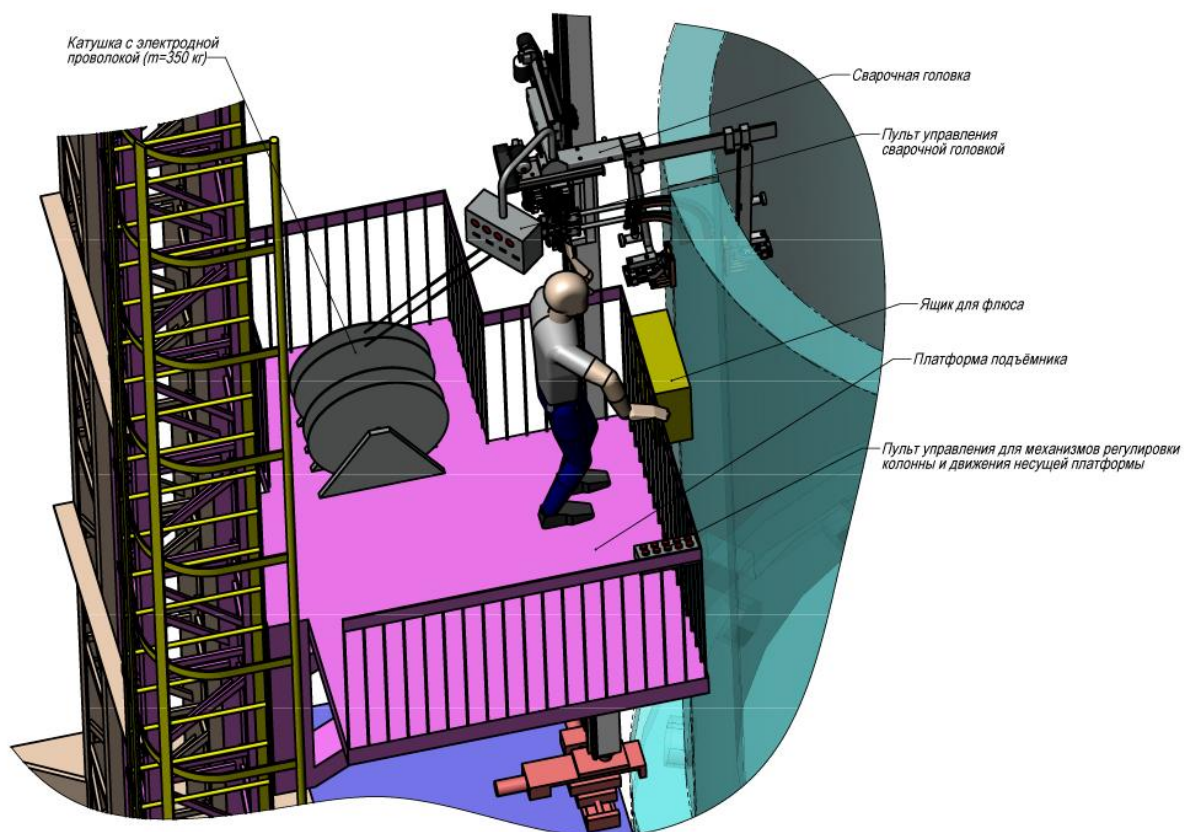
«Сварка обечаек установкой на платформе»[21]
